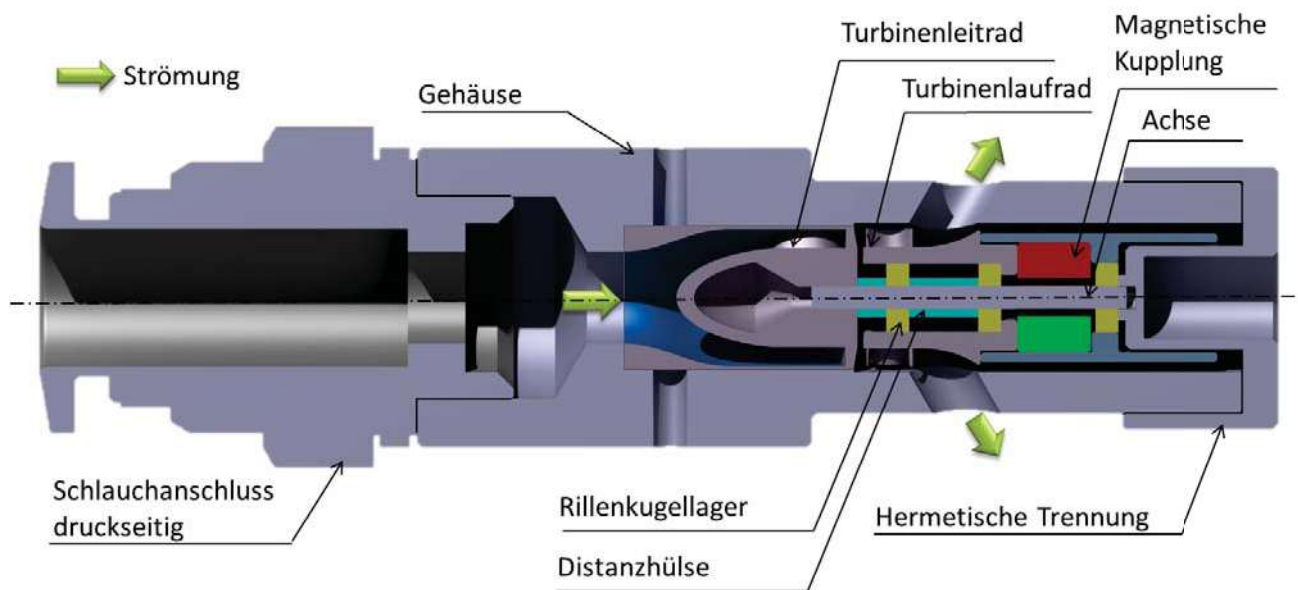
Baugruppe mit allen Komponenten der zusammgebauten Turbine
